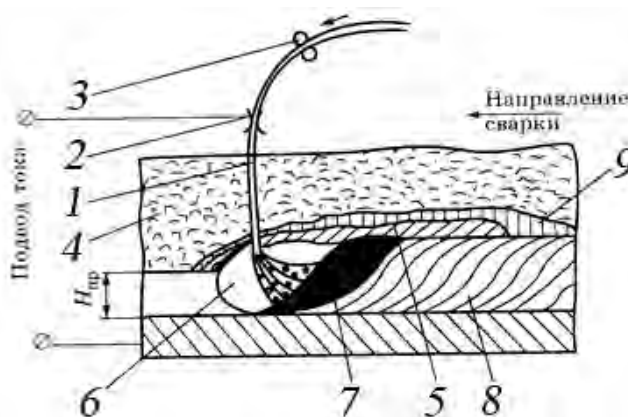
Схема процесса сварки под флюсом
